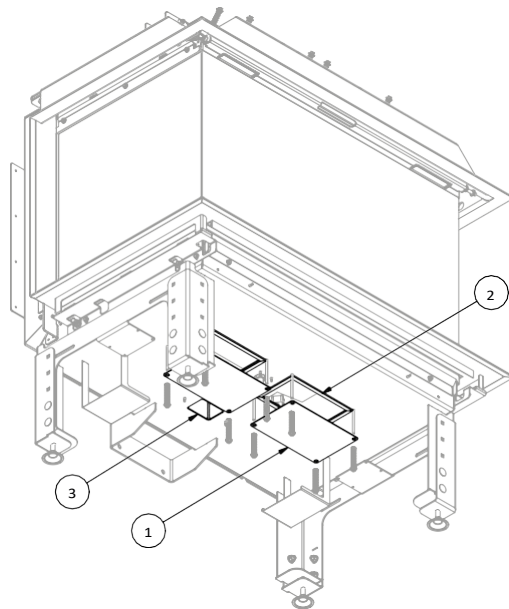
разборка взрывозащитных заслонок (из ревизий): 1 - пластина заслонки; 2 - прокладка; 3 - канал пилотной горелки
